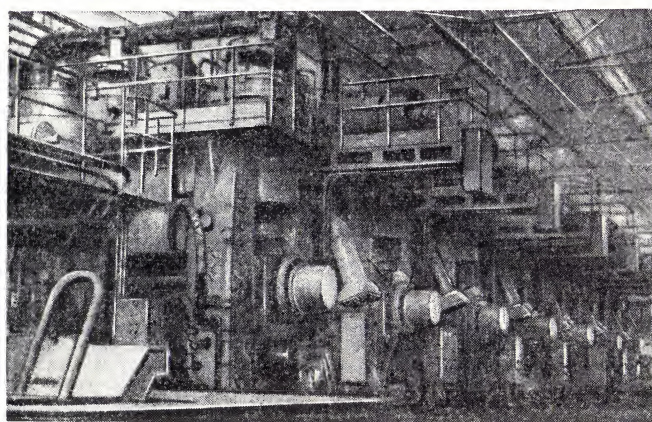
Непрерывный широкополосовой стан горячей прокатки.
